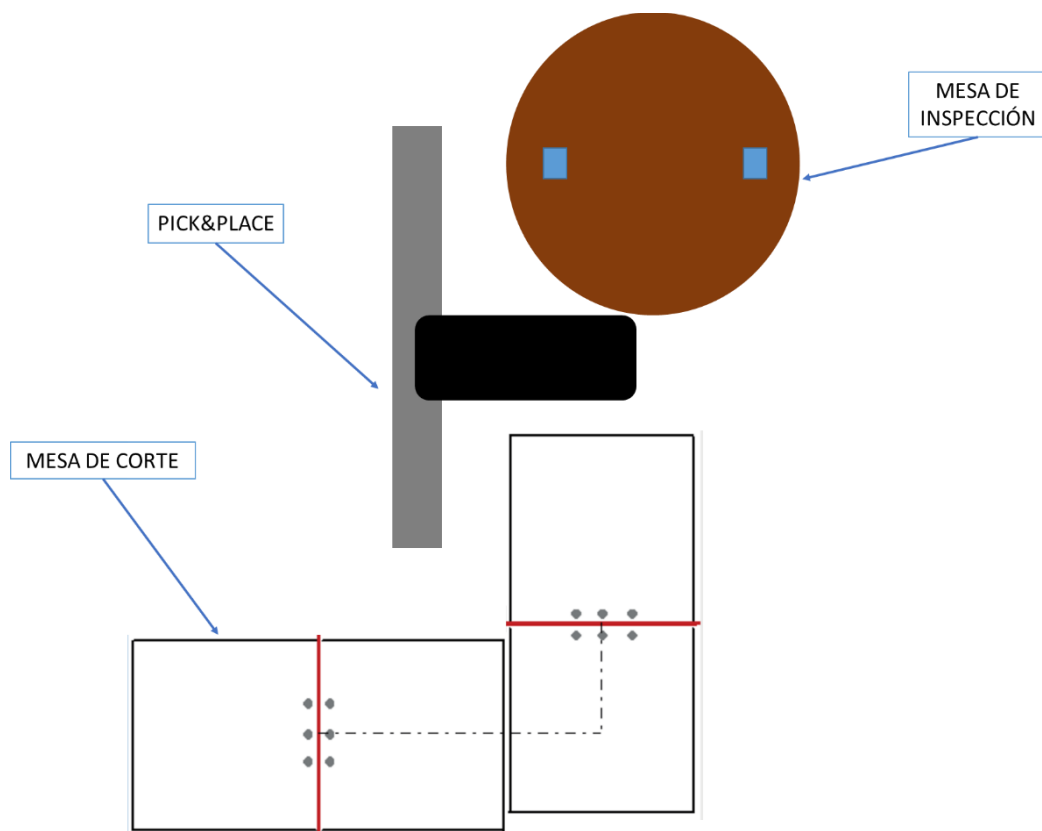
Layout general que incluye la mesa de corte, mesa de inspección y el pick&place
